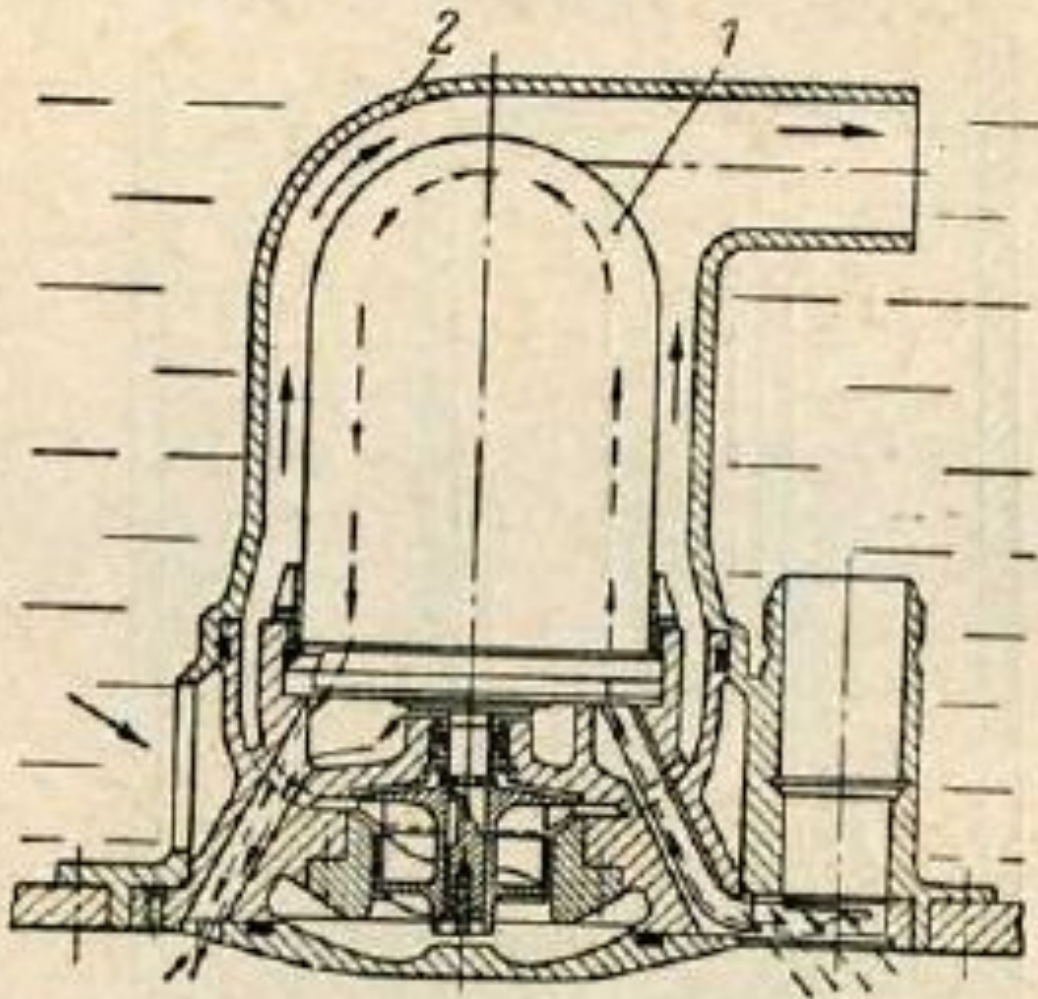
Кессонный ЭЦН с верхним расположением рабочего колеса:
